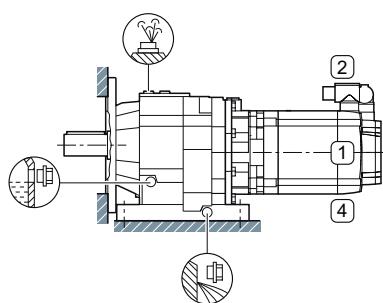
Einbaulagen für Servo-Stirnradgetriebemotoren Z und D, Fußausführung, Baugrößen 39 - 129, 2-stufig und 3-stufig
